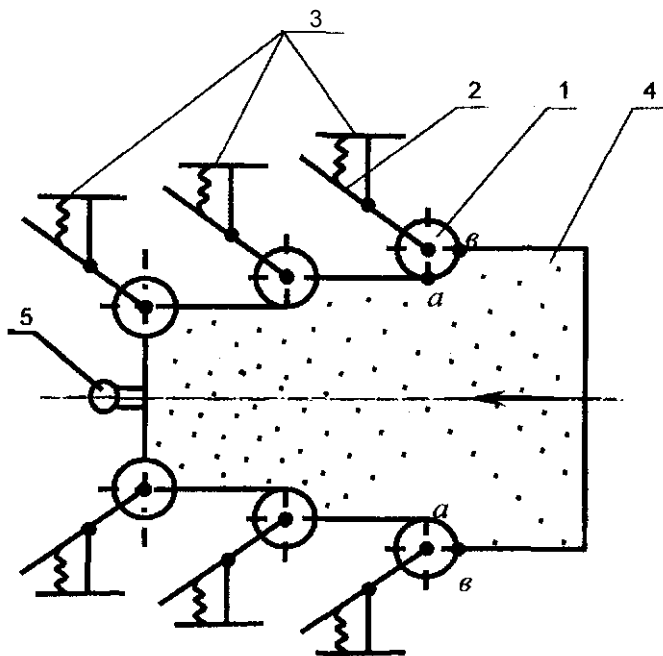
Устройство для выбивки литейных форм (вид сверху): 1 - выбивные валки; 2 - нажимные устройства; 3 - рама; 4 - форма; 5 - отливка
